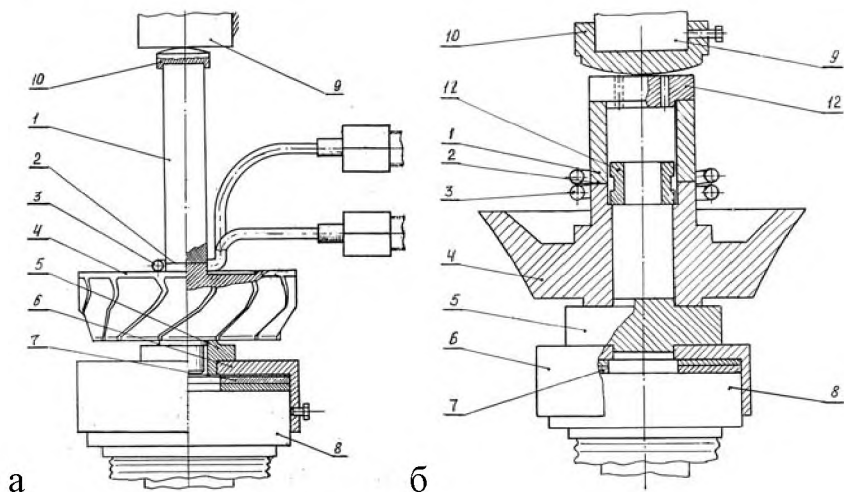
Оснастка для диффузионной сварки рабочих колес роторов турбин с валами сплошного сечения: 1 – вал ротора турбины, 2 – никелевая прокладка, 3 – индуктор, 4 – рабочее колесо ротора турбины, 5 – опорная втулка, 6 – центрирующий стакан, 7 – регулировочные прокладки, 8 – шток силопровода, 9 – упор вакуумной камеры, 10 – сферический наконечник
